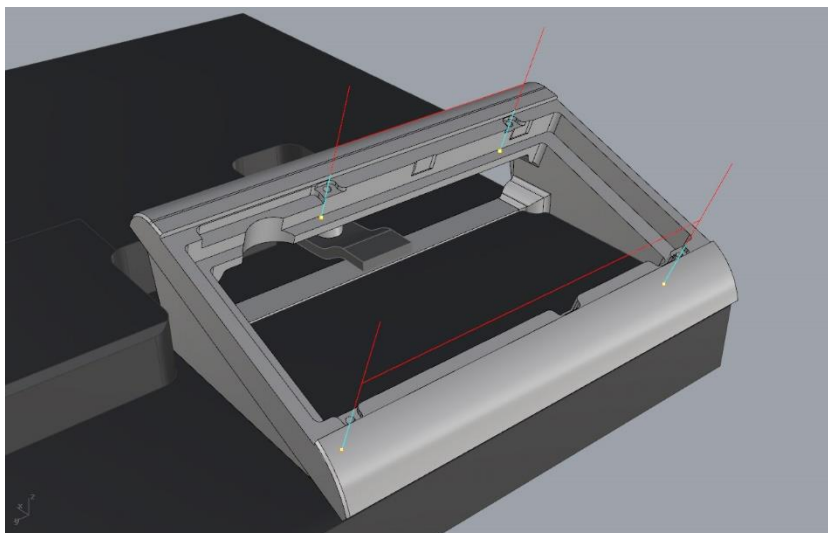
Druhé upnutí – dokončování fréza 20 mm – Axis Profiling
